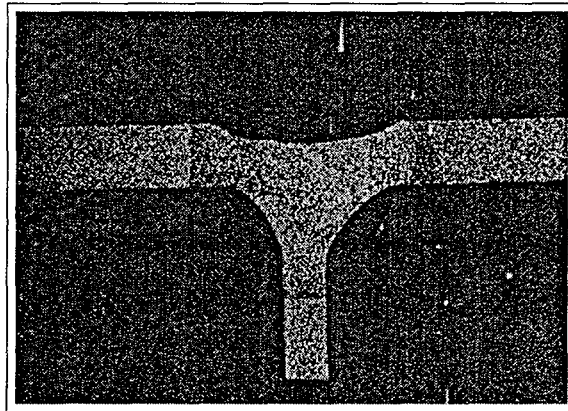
교차점 용접단면 (Cross Section of Weld)
